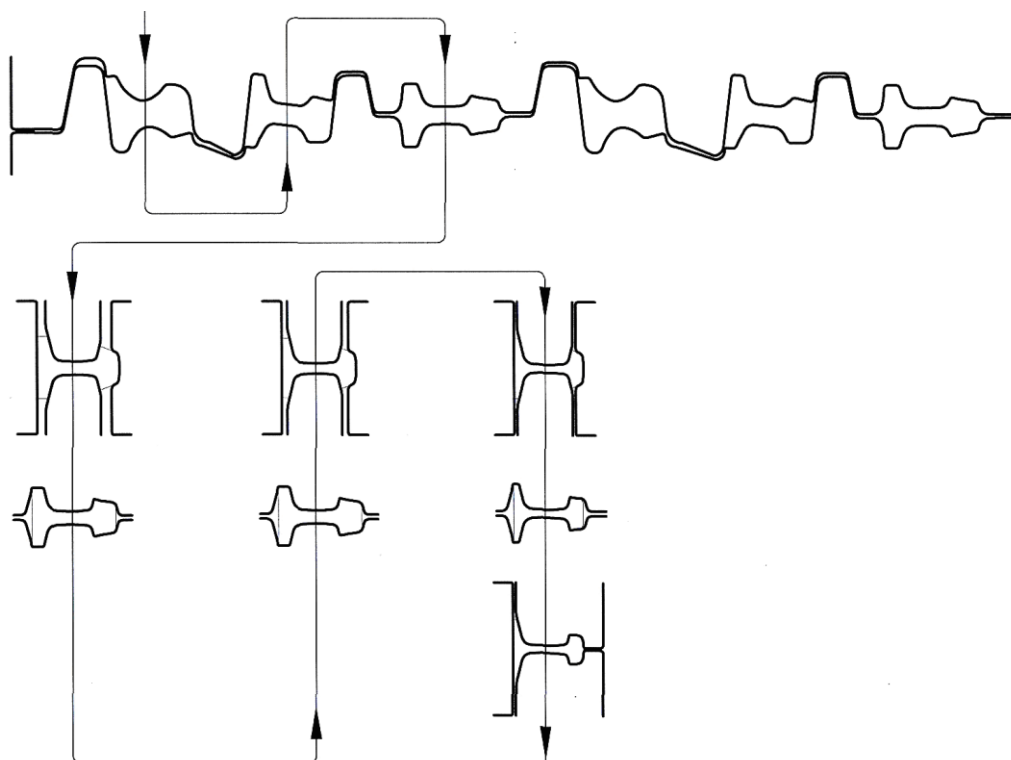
Схема калибровки валков ОАО «ЕВРАЗ ЗСМК» на стадии формирования рельсового профиля
